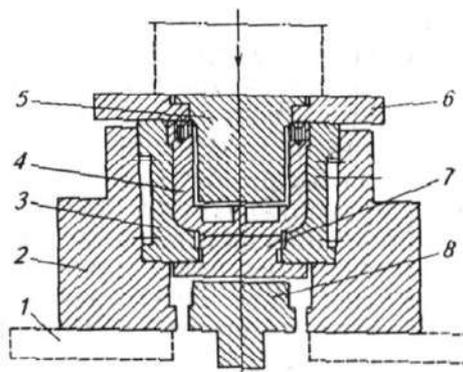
Схема пресс-формы для обжатия корпусов насосов:
